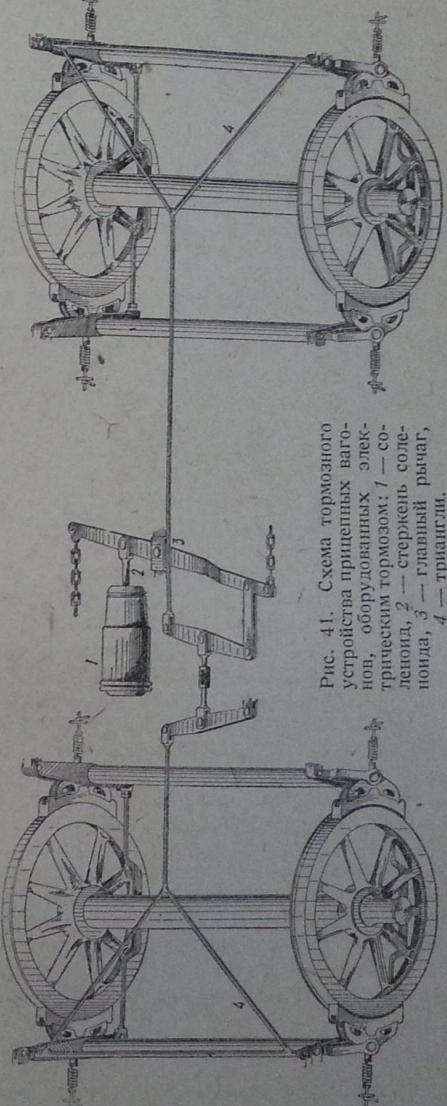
Схема тормозного устройства прицепных вагонов, оборудованных электрическим тормозом: 1 — соленоид, 2 — стержень соленоида, 3 — главный рычаг, 4 — трианглы.
